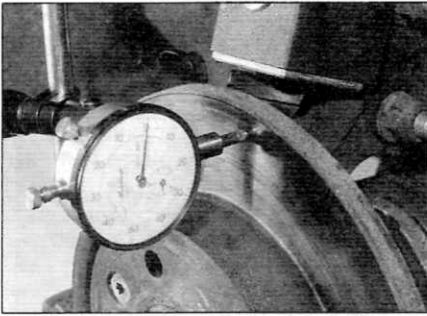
Проверка биения диска с помощью стрелочного индикатора
